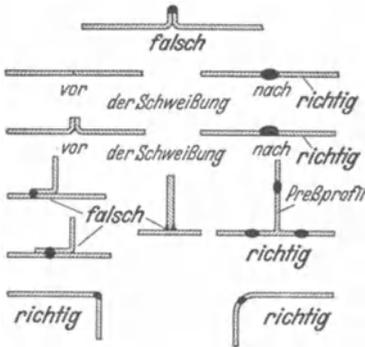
Schweißnahtanordnungen für Elektron.
